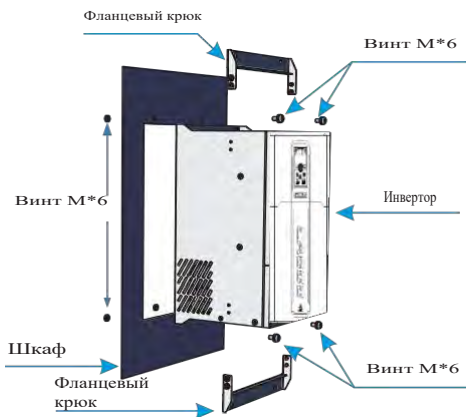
Чертеж сквозного монтажа листовой металлоконструкции
